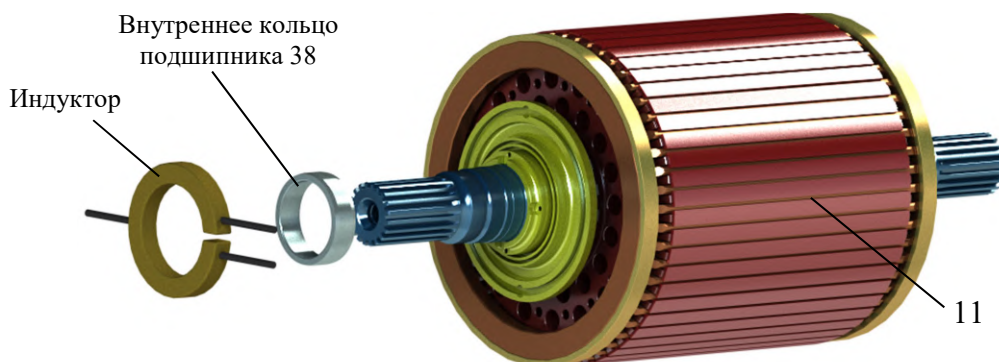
Демонтаж внутреннего кольца подшипника
